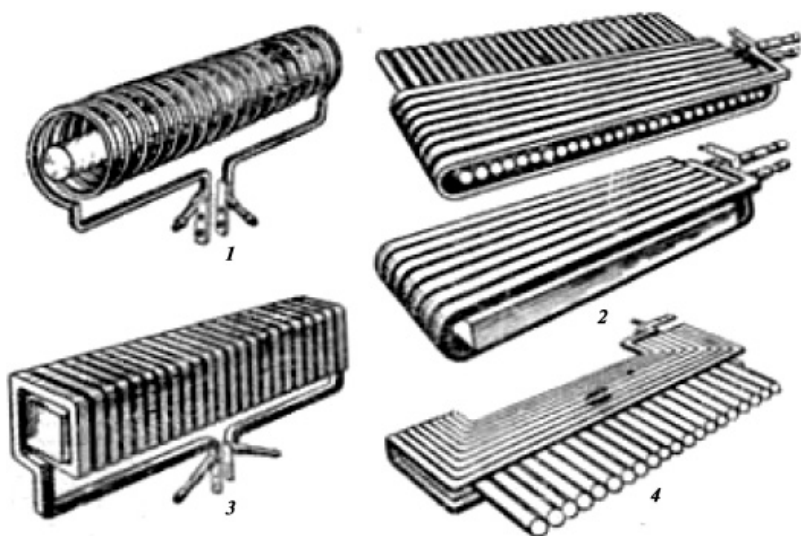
Формы индукторов и расположение в них нагреваемых заготовок
